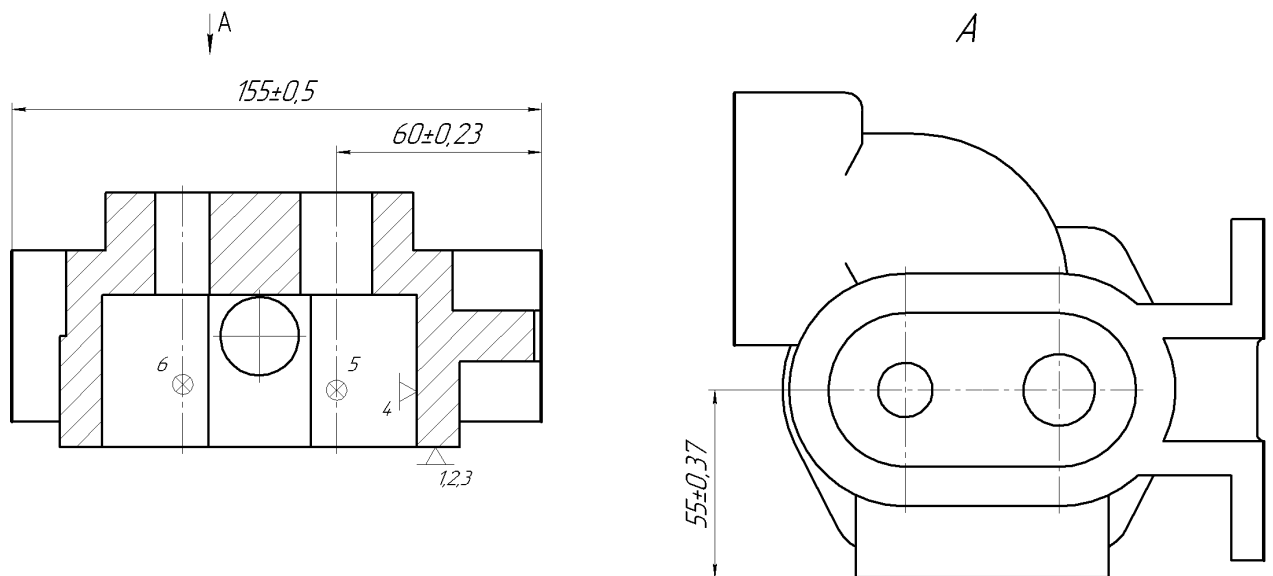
Схема базування заготовки на операції №005 «Горизонтально-фрезерна».
